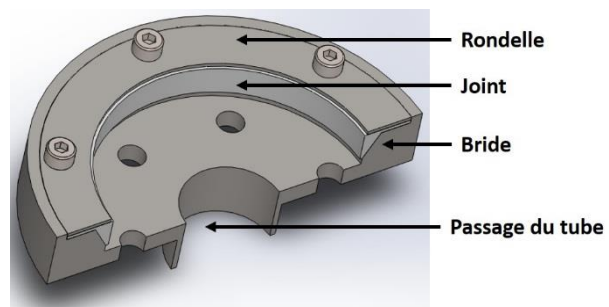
Vue en coupe du dessin de la bride inférieure.
